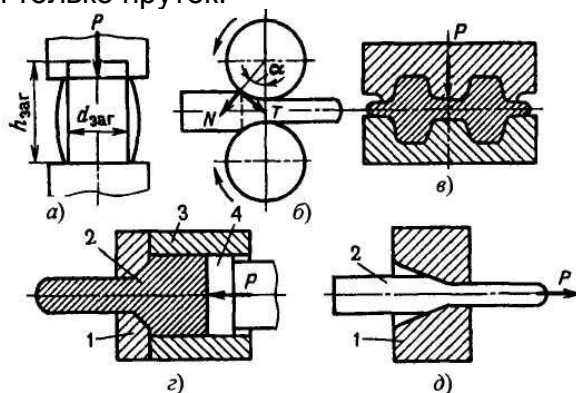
Основные схемы деформирования в обработке металлов давлением:
